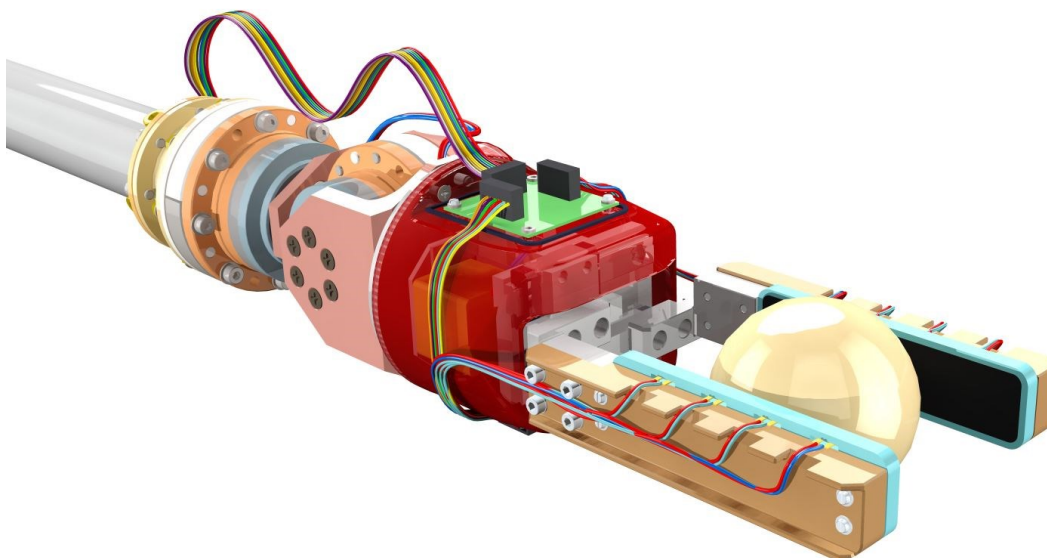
Vedení kabeláže k motoru efektoru
